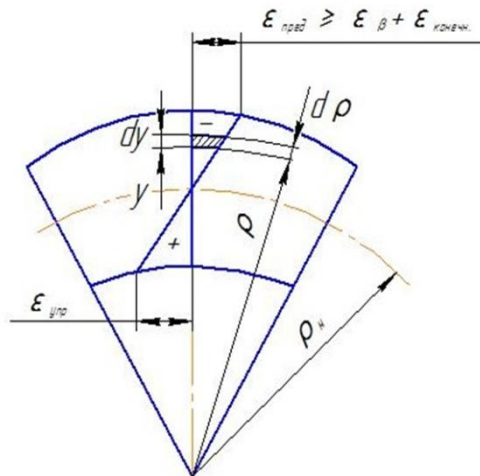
Расчетная схема гибки для определения толщины упругой планки
